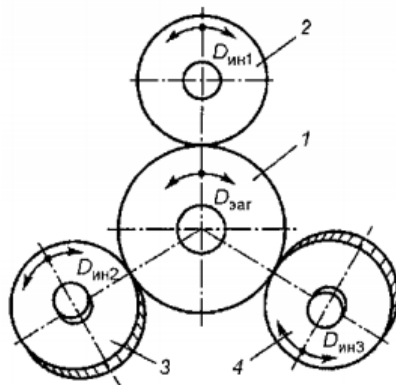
Схема обробки зубів колеса трьома притирами:
